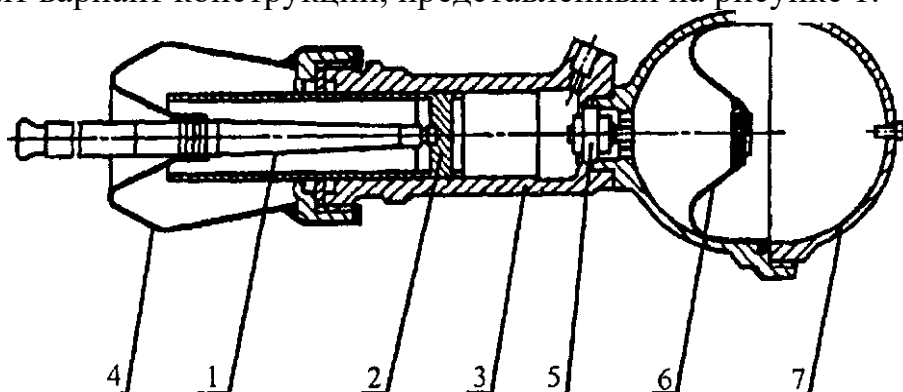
Общий вид ПГА [5]: 1 - толкатель; 2 - поршень; 3 - цилиндр; 4 - уплотнительный чехол; 5 - дросселирующая система амортизатора; 6 - эластичная диафрагма; 7 - пневматический баллон
